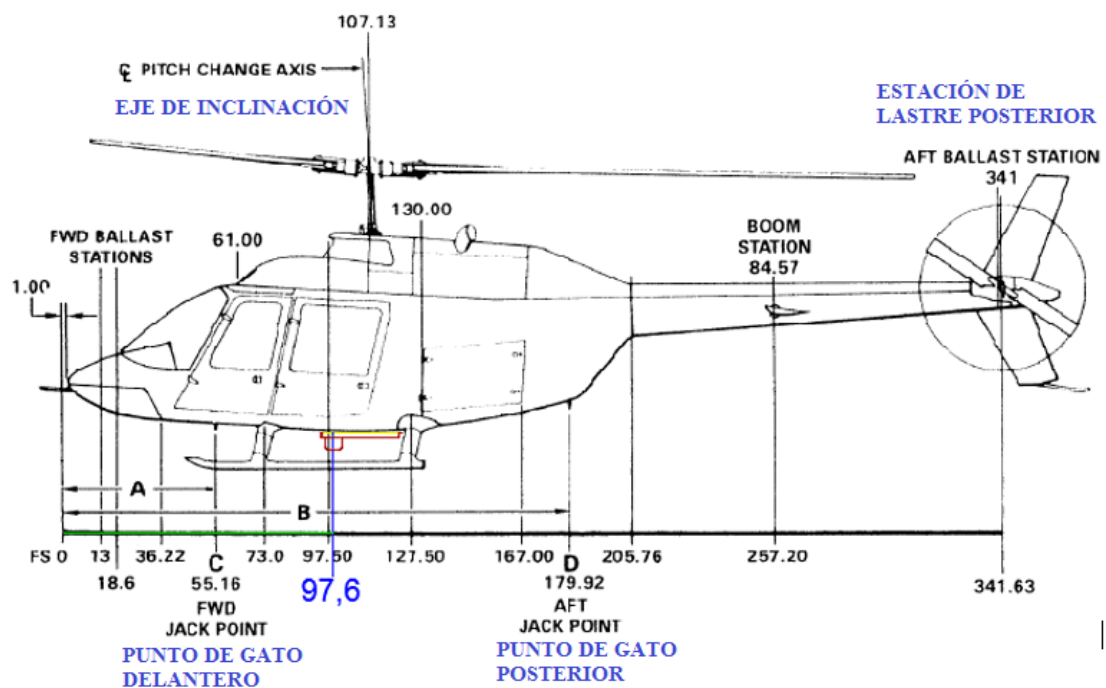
Datum (referencia) y brazo al centro de masa del soporte [23].
